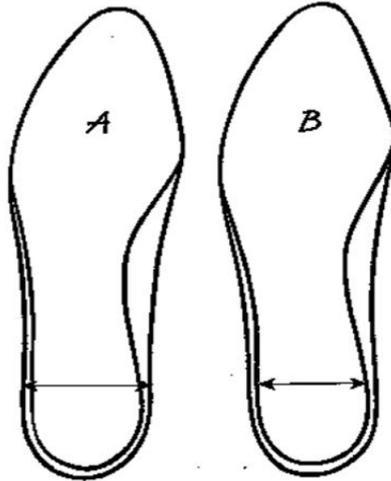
A: Pestaña de la horma, B: Anchura del talón sobre la superficie plantar
